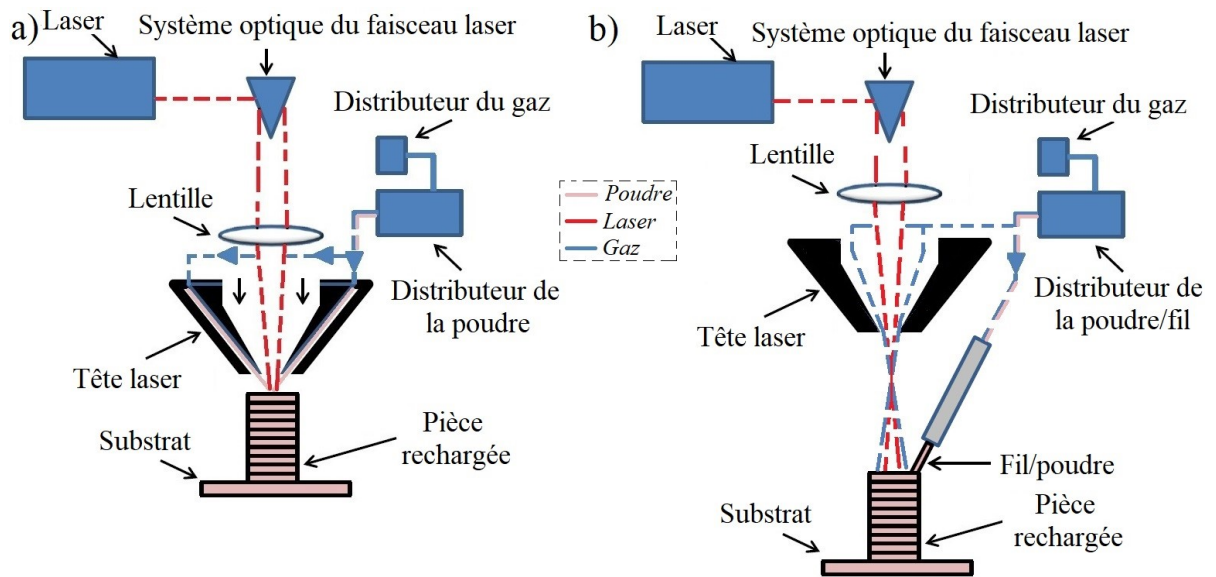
Schéma de principe de fabrication par fusion de poudre injectée coaxialement (a) et de fil/poudre injectée latéralement (b)
